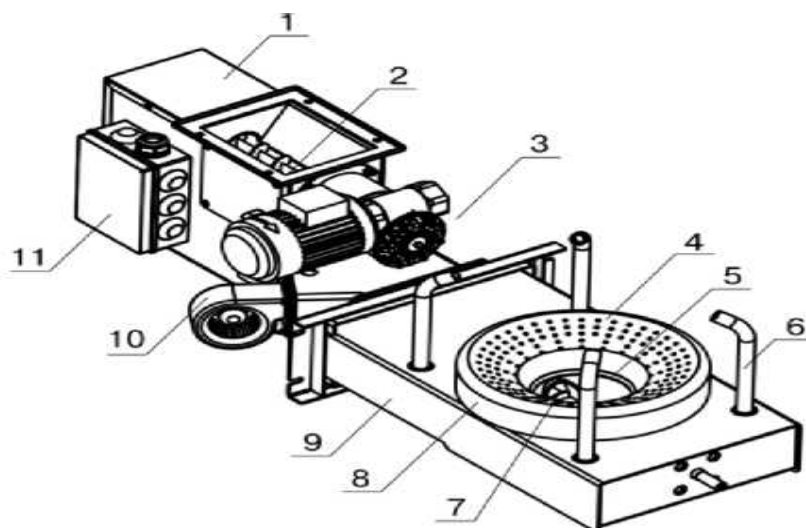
Пеллетная горелка с приводом. (1 – корпус привода. 2 – Шнековый механизм. 3 – Электродвигатель. 4 – Чаша. 5 – Нагревательная элемент. 6 – Трубки подачи вторичного воздуха. 7 – Ворошитель. 8 – Тарелка. 9 – Корпус горелки. 10 – Электровентилятор. 11 – Коробка распределительная).
